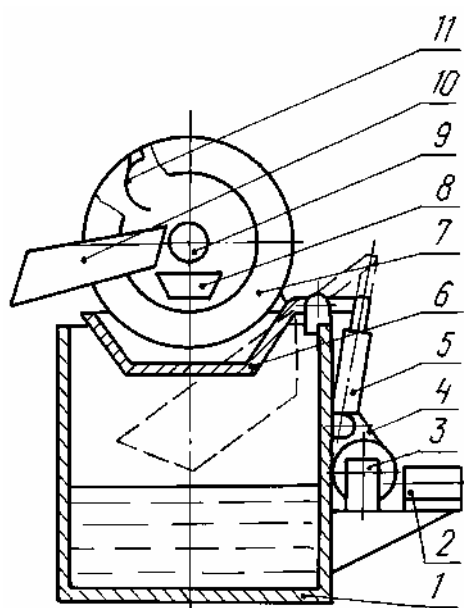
Установка для очистки метизов: 1 – ванна; 2 – электродвигатель; 3 – редуктор; 4 – передача цепная; 5 – пневмоцилиндр; 6 – ванна подвижная; 7 – барабан перфорированный; 8 и 10 – лотки; 9 – гидрант; 11 – пластина разгрузочная
